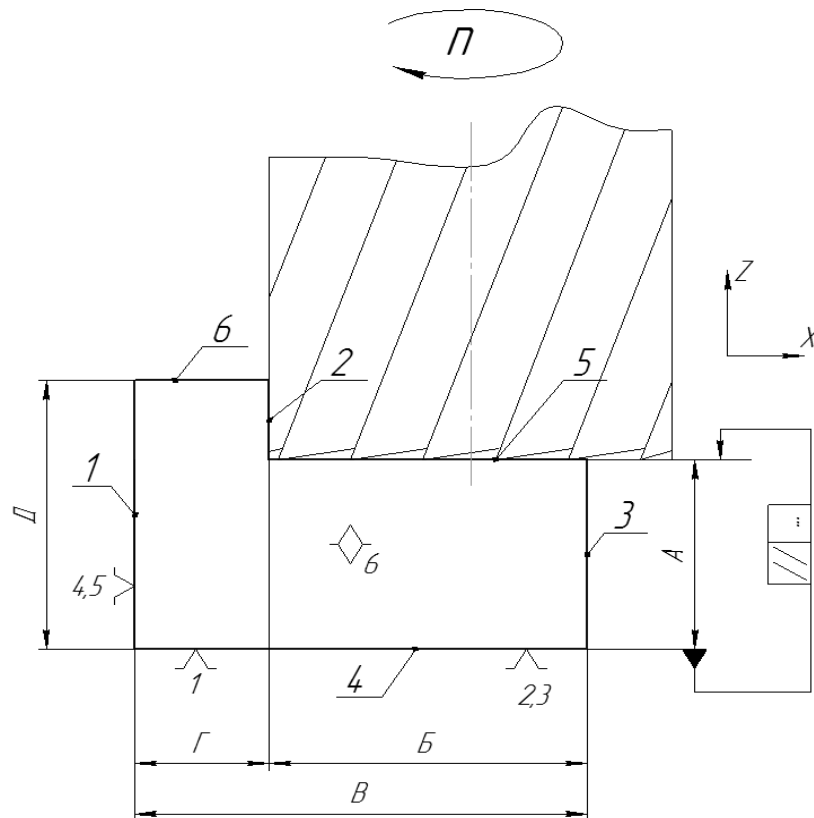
Операционный эскиз вертикально-фрезерной операции
